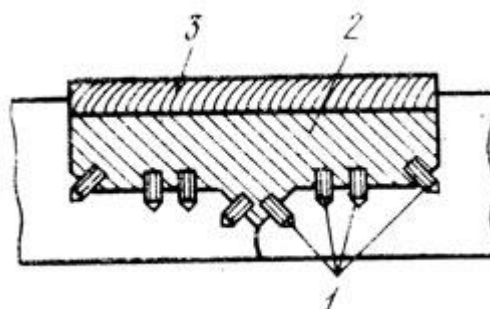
Подготовка чугунного изделия к холодной сварке со стальными шпильками: 1 - стальные шпильки, 2 - стальная связь, 3 - наплавка медно-никелевым электродом
